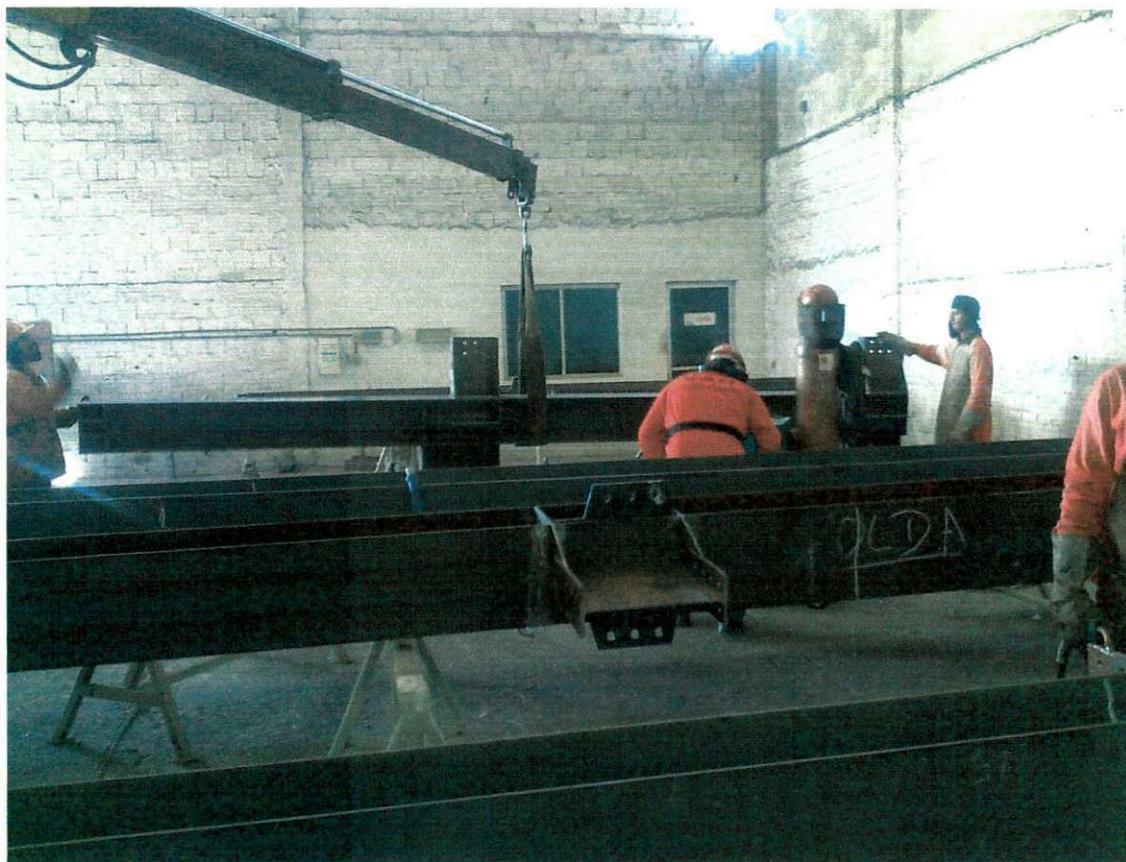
Armação dos pilares do 6º e 7º pavimento da obra do shopping Boa Vista.
